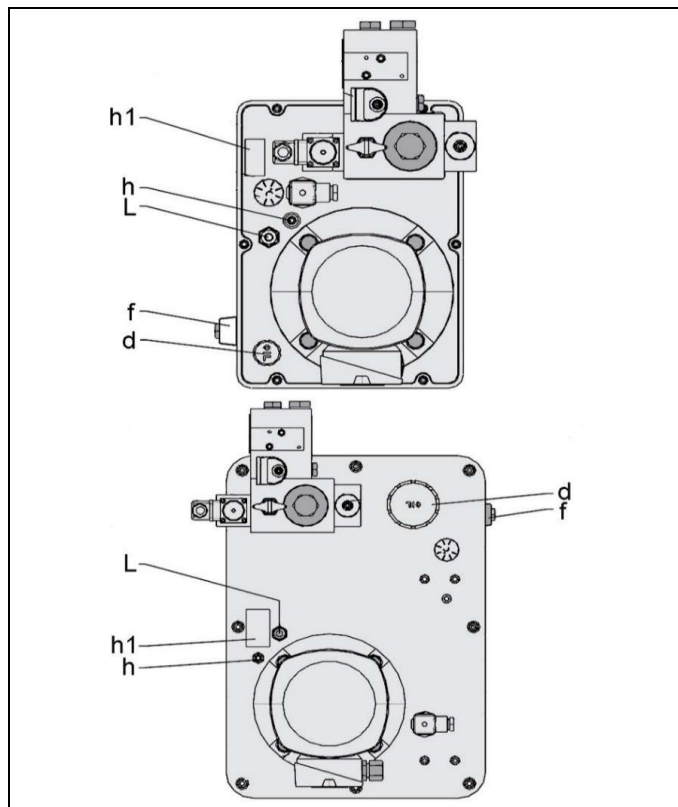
Figure sur le couvercle du groupe hydraulique V11/27/40/63
